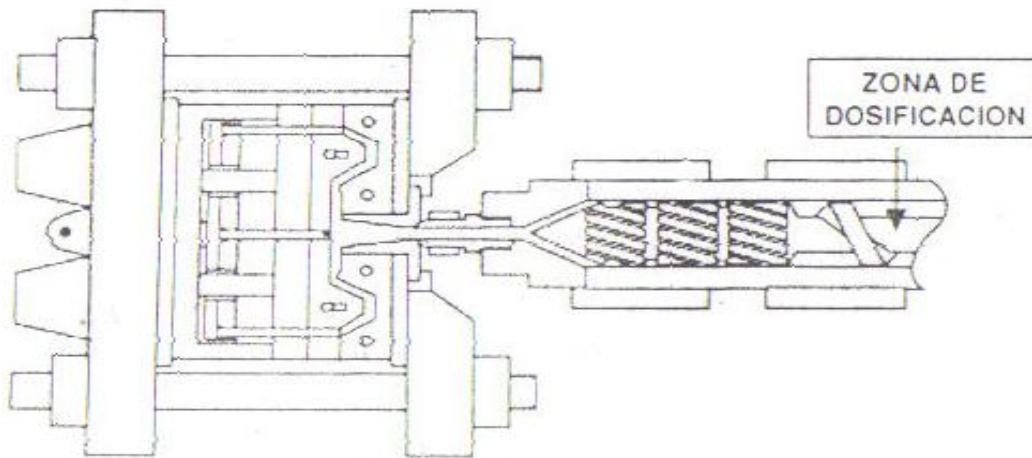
Forma en la cual la boquilla debe de coincidir con el bebedero del molde.⁽¹⁰⁾
